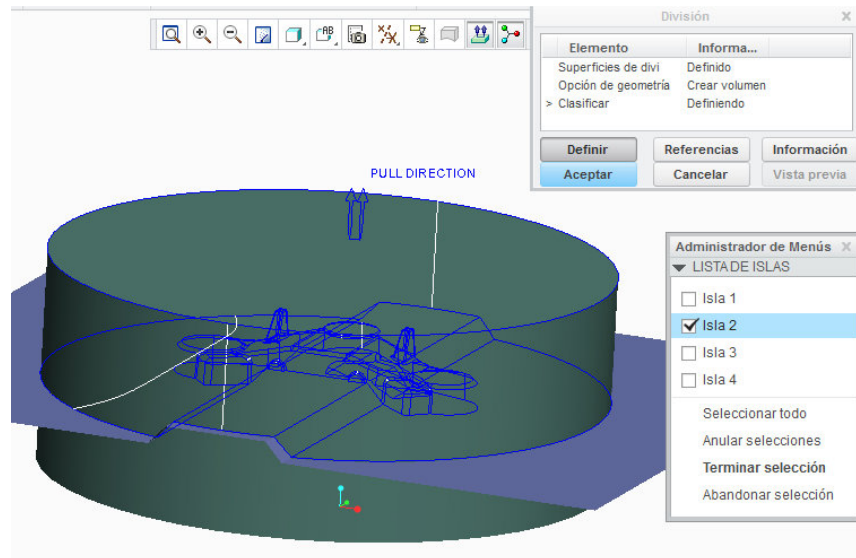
Seccionado de matrices mediante el módulo de molde en Creo 2.0
